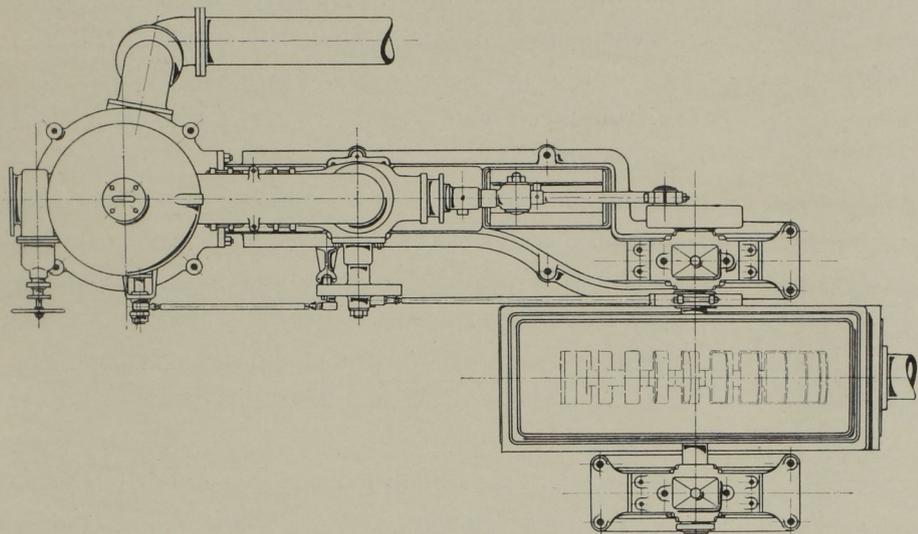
Grundriss der Pumpe mit Antriebsrad.
